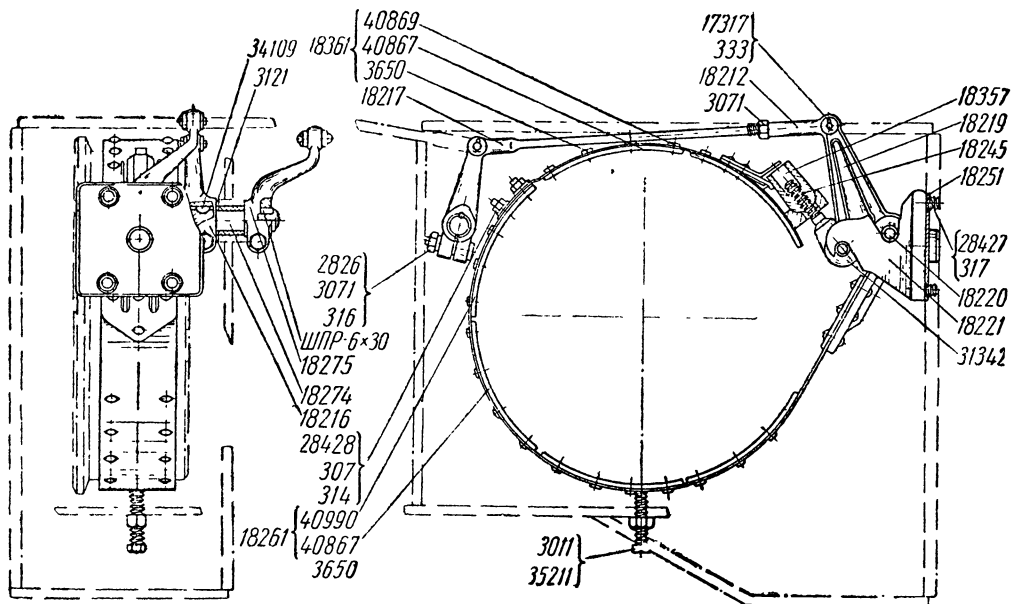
Вспомогательный гидравлический механизм — комплект 17356.
